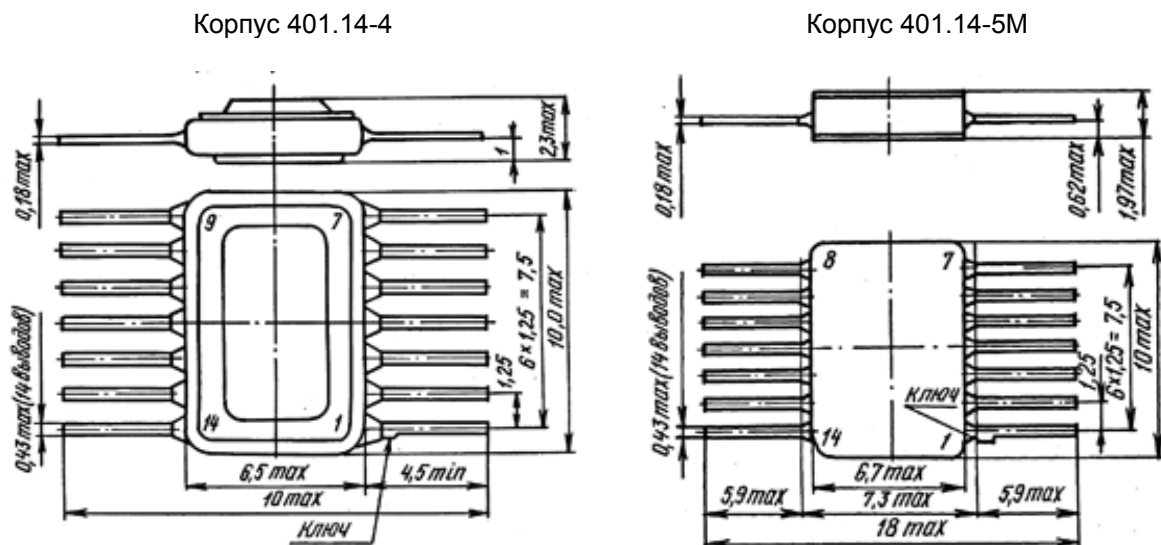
Габаритные чертежи корпусов 401.14-4 и 401.14-5M
